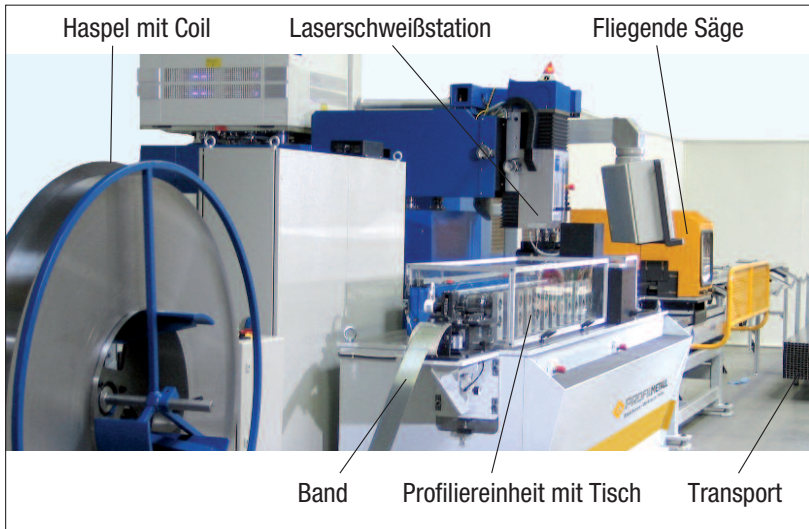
Aufbau einer typischen industriellen Walzprofilierstrecke [54]
